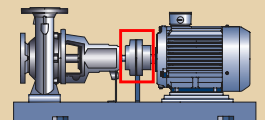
Pumpe auf Grundplatte mit Ausbaukupplung
